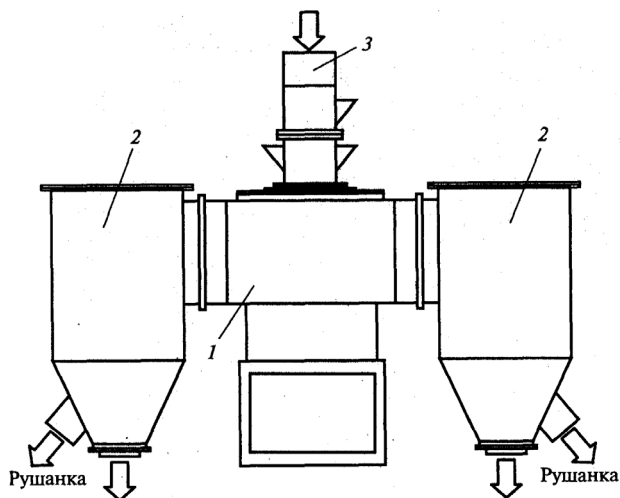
Центробежная обрушивающая машина РЗ-МОС:
